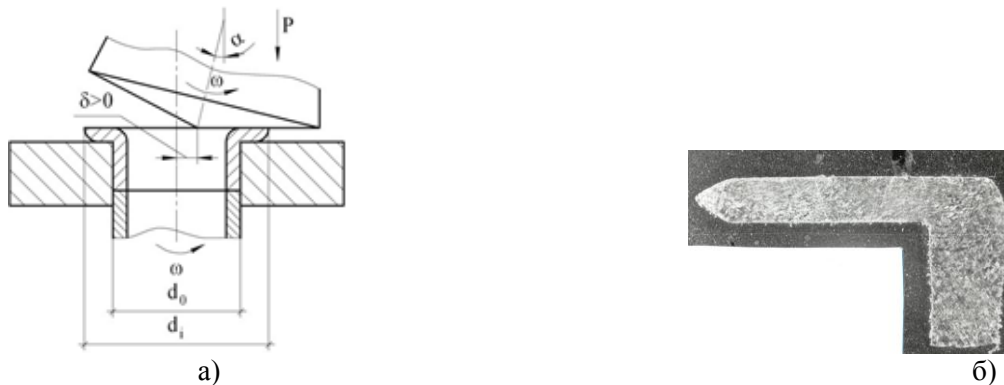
Схема висаджування зовнішнього фланця заготовки методом штампування обкочуванням а) і форма перерізу сформованого фланця б)
